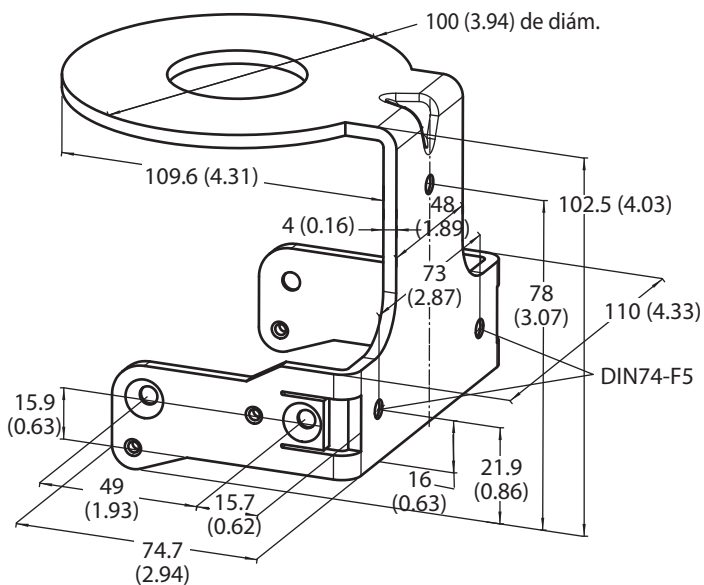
Esquema de dimensiones, juego de montaje 3 442L-AMBSZMN3
